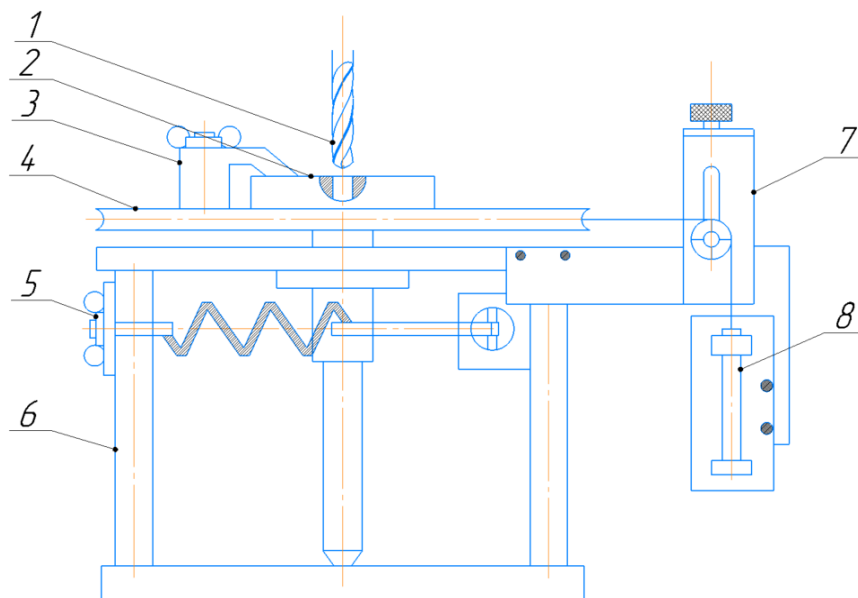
Схема установки для исследования СОТС при сверлении:
